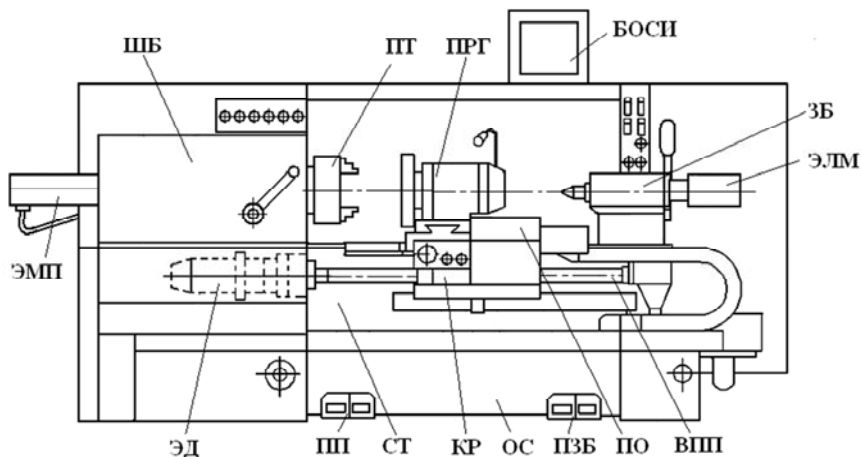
Внешний вид токарного станка модели 16K20Ф3С32:
